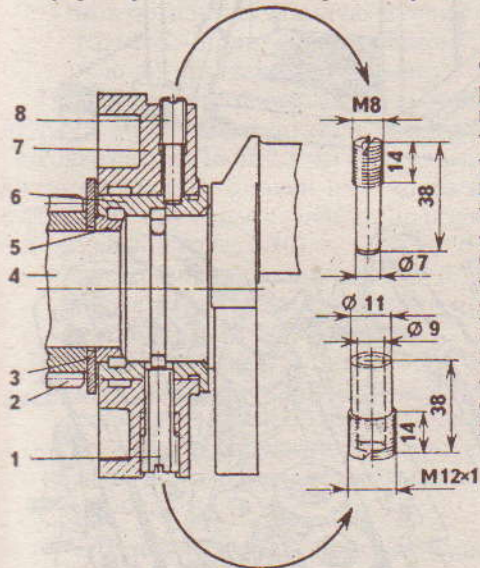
Фиксация коренного подшипника: 1 - трубка-фиксатор; 2 - шестерня распределительного вала; 3 - опорная шайба; 4 - коленчатый вал; 5 - упорное кольцо; 6 - подшипник; 7 - передняя опора; 8 - новый фиксирующий штифт
